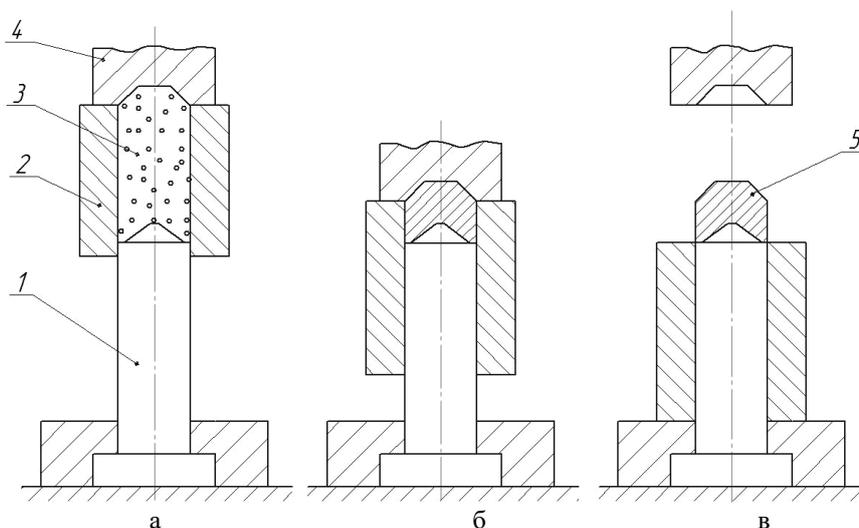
Схема прессования заготовки: а – заполнение; б – прессование; в – выталкивание; 1 – пуансон, 2 – нижняя полуматрица, 3 – порошок, 4 – верхняя полуматрица, 5 – заготовка
